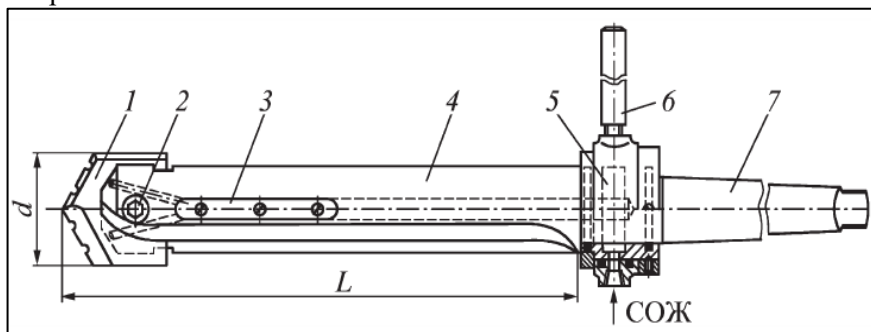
Сборное перовое сверло для глубоких отверстий:
